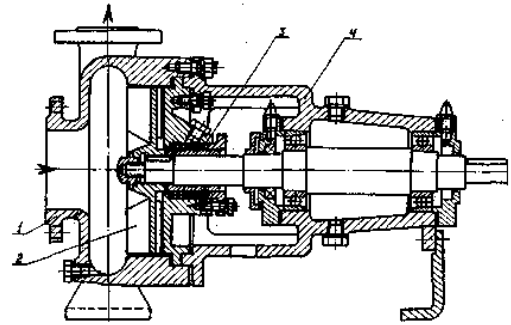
Конструкція насоса ВВН: 1 – корпус; 2 – робоче колесо; 3 – ущільнення кінцеве; 4 – корпус підшипників
